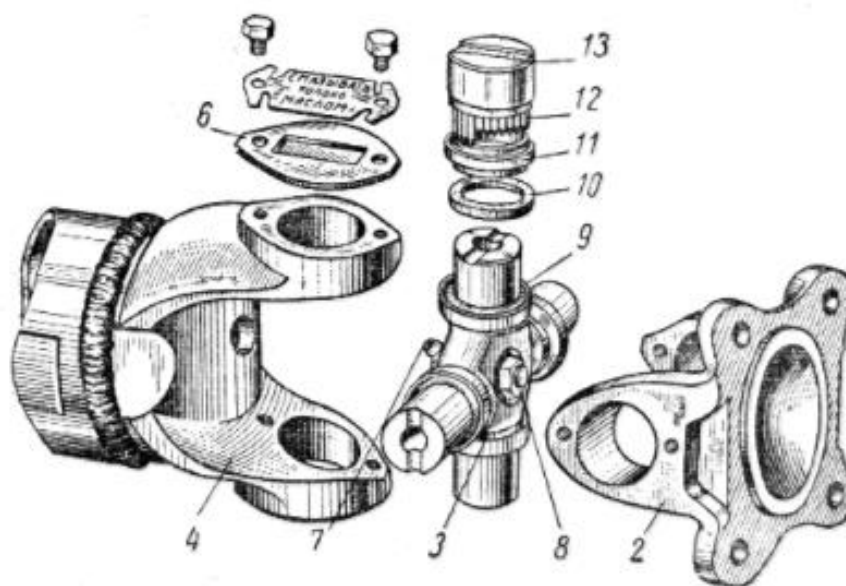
Карданный шарнир неравных угловых скоростей: 2 и 4 – ушки карданных вилок; 3 – крестовина; 6 – стопорная пластинка; 7 – центральная масленка; 8 – предохранительный клапан; 9 – металлический корпус; 10 – резиновый сальник; 11 – опорная шайба; 12 – игольчатый подшипник; 13 – стальной стакан
